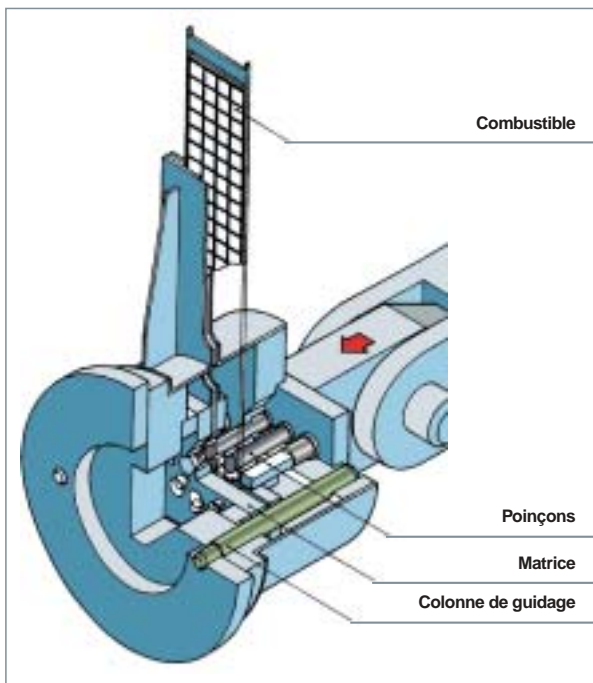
Vue en coupe d'une machine de poinçonnage de plaques de combustible.
